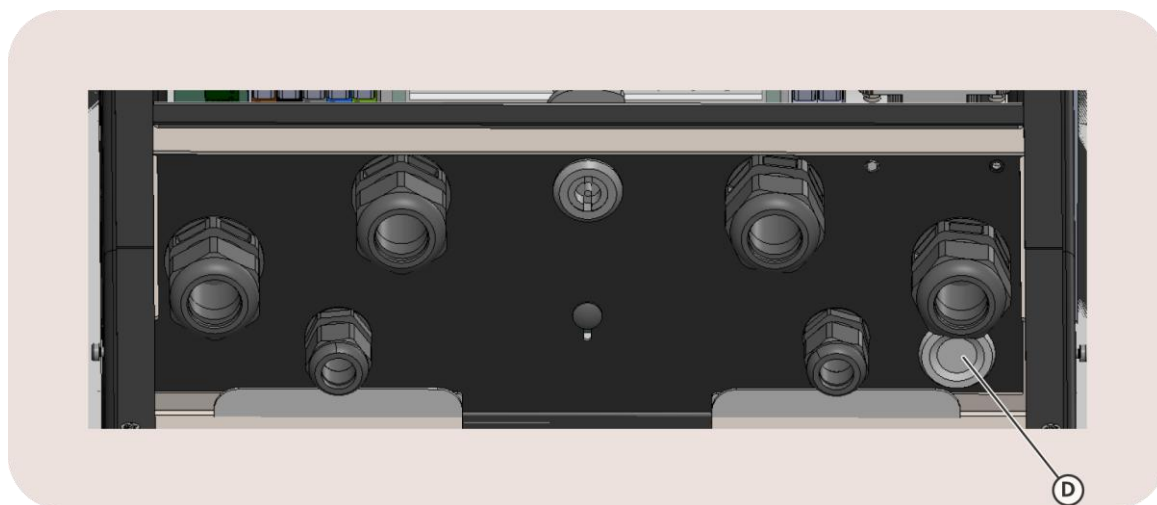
Blick auf die Tülle (D) für das Kabel zur LED-Platine.
